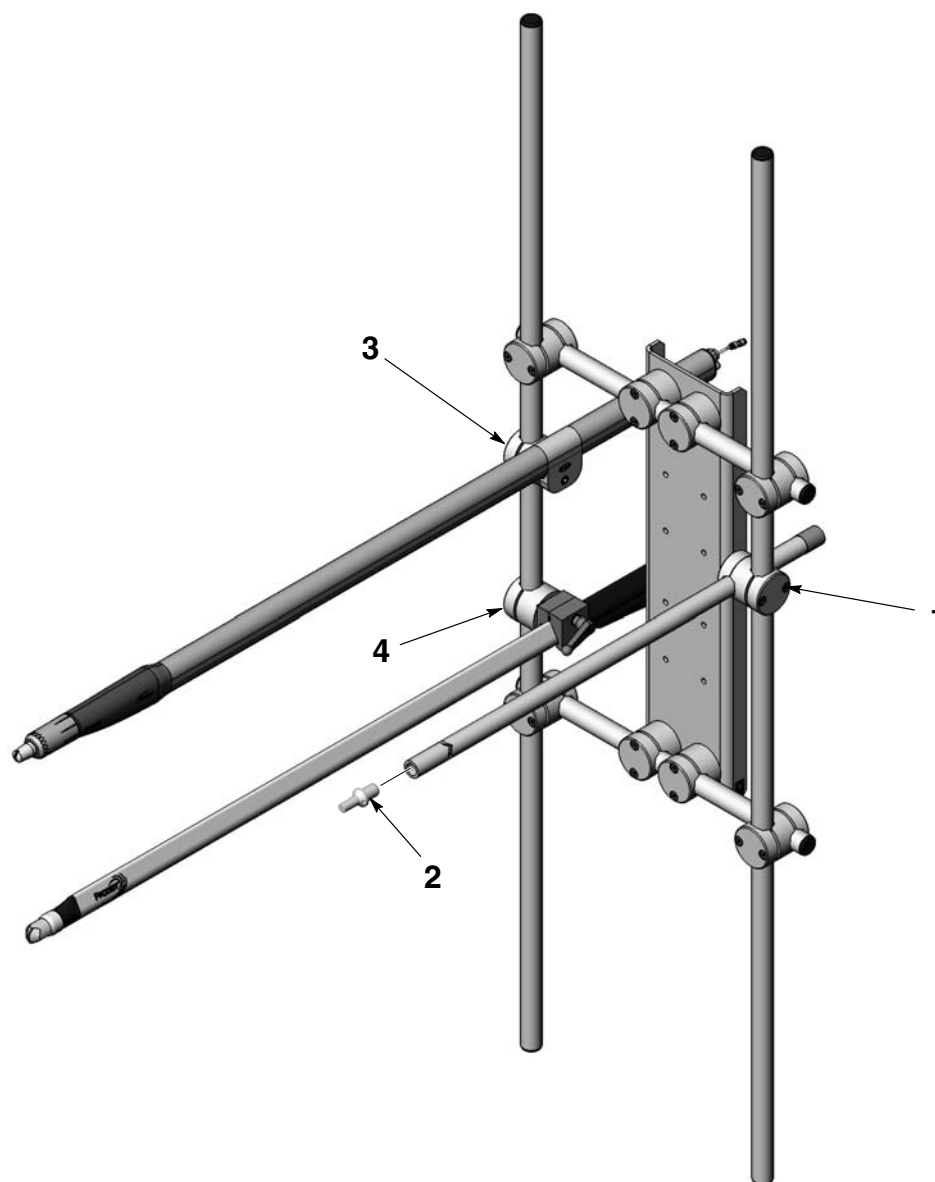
Kits supports de pistolet horizontaux et de fixation sur barre
